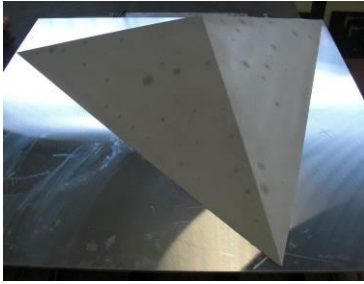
Tiefziehwerkzeug ©BAUER THERMOFORMING
